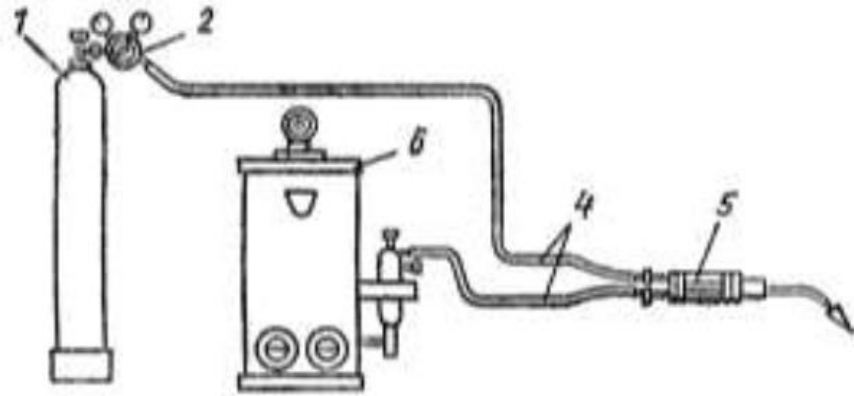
Схема поста газового зварювання: 1 – балон з киснем; 2 – кисневий редуктор; 3 – затвор; 4 – шланги; 5 – пальник; 6 – ацетиленовий генератор
